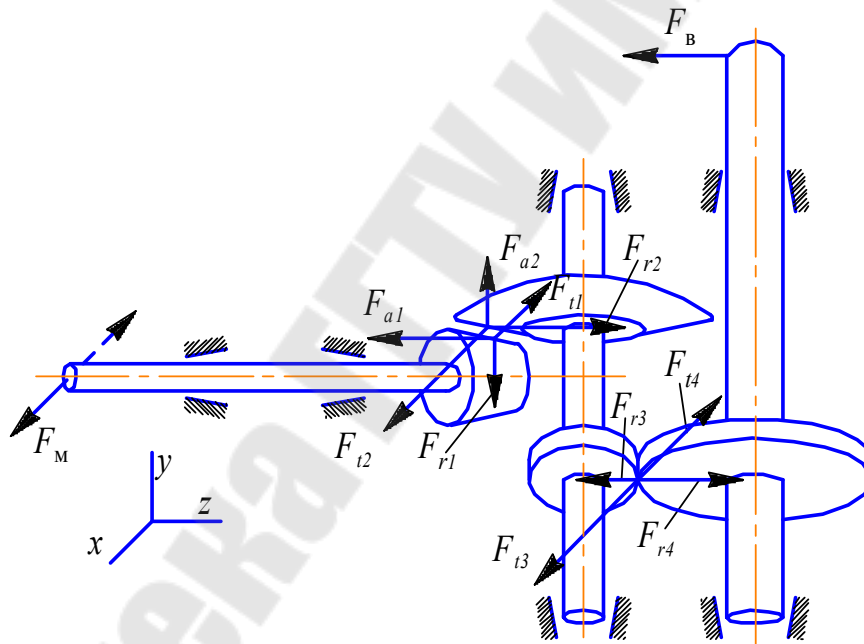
Схема нагружения валов двухступенчатого цилиндрического редуктора
